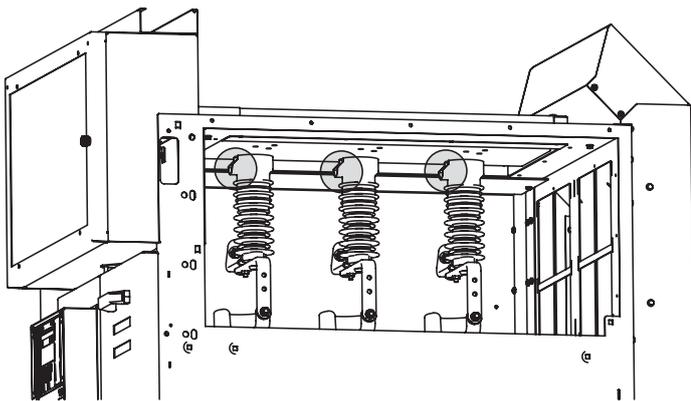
Terminales del seccionador para las conexiones en cable del indicador de tensión
